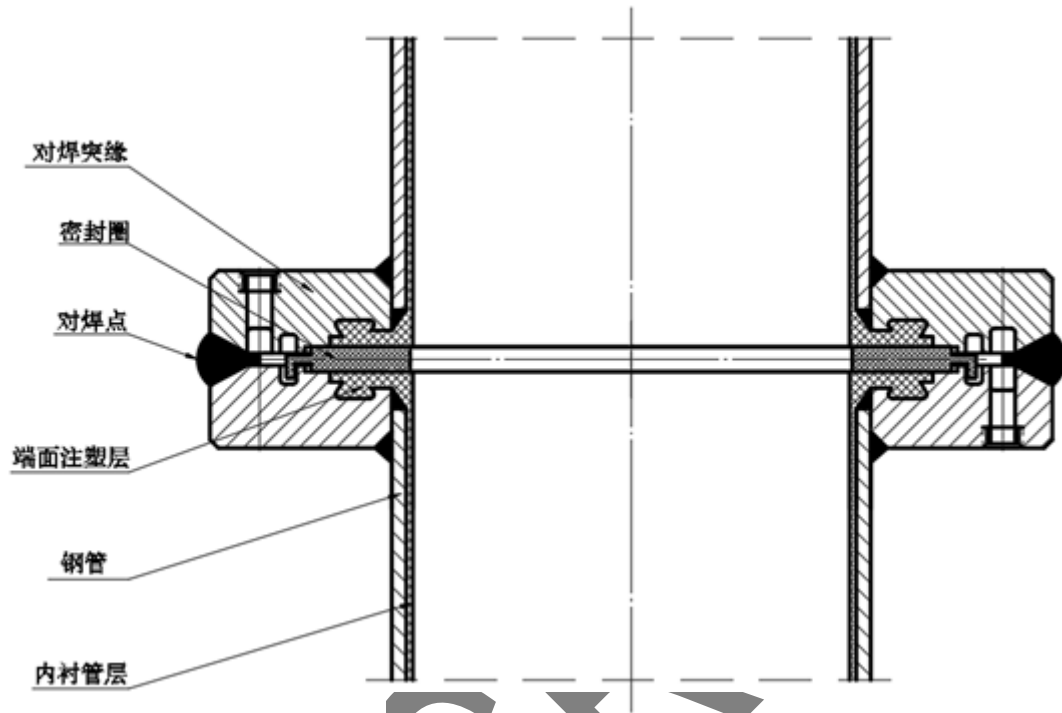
全防腐钢塑复合管对焊突缘连接结构示意图
